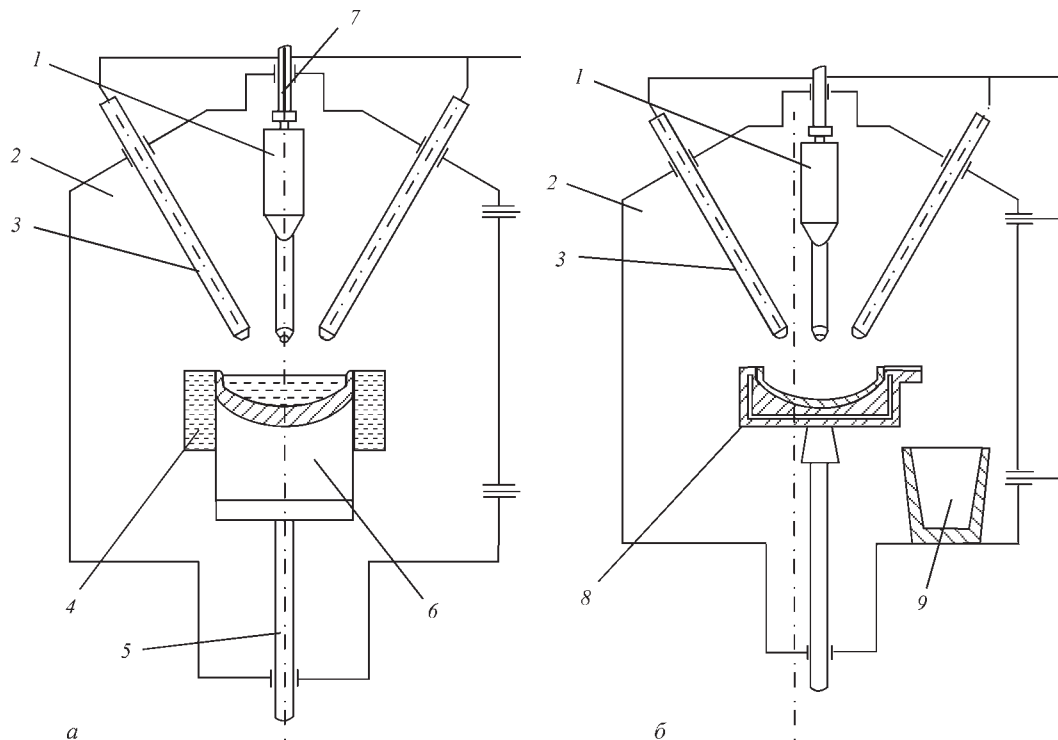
Схеми переплаву в наскрізний мідний водоохолоджуваній кристалізатор (а) та в мідному водоохолоджуваному тиглі (б): 1 — заготовка; 2 — плавильна камера; 3 — плазмотрон; 4 — кристалізатор; 5 — зливков; 6 — механізм витягування зливка; 7 — механізм подачі заготовки; 8 — тигель; 9 — виливниця
